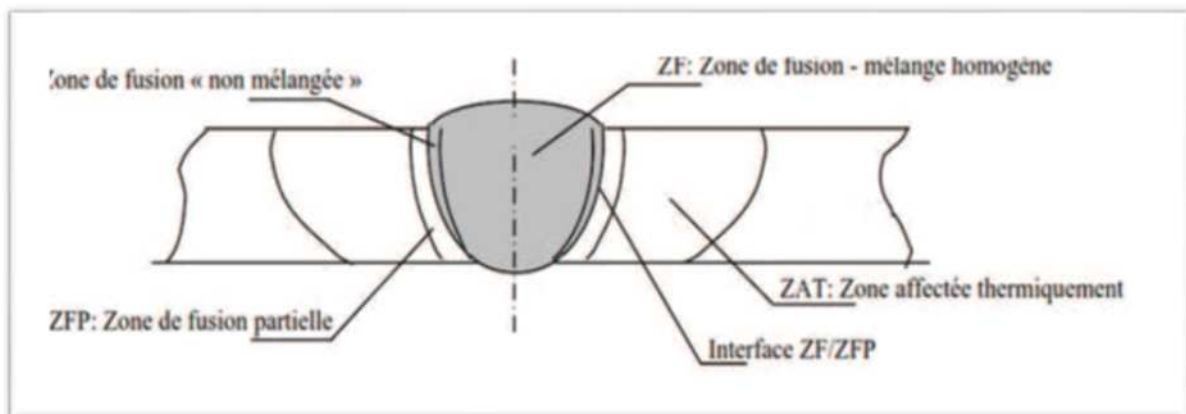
Les différentes zones caractéristiques d'une soudure par fusion [9].
